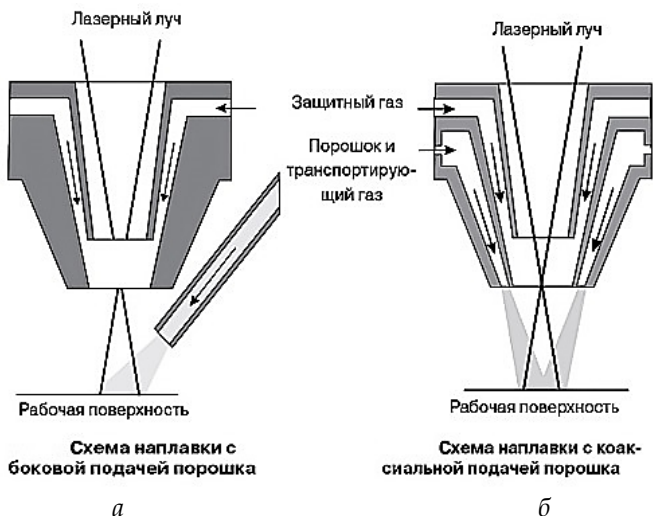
Схема лазерной наплавки с боковой (а) и коаксиальной (б) подачей порошка [6]
